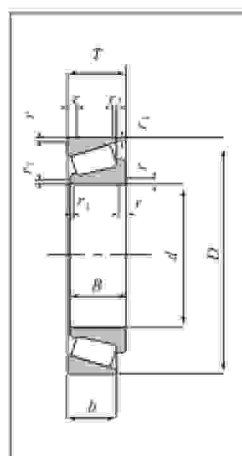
Dimensiones Principales de los Rodamientos de Rodillos Cónicos.
